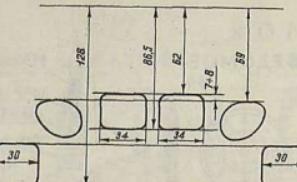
Развертка цилиндра двигателя ИЖ-56, подготовленного для соревнований.
